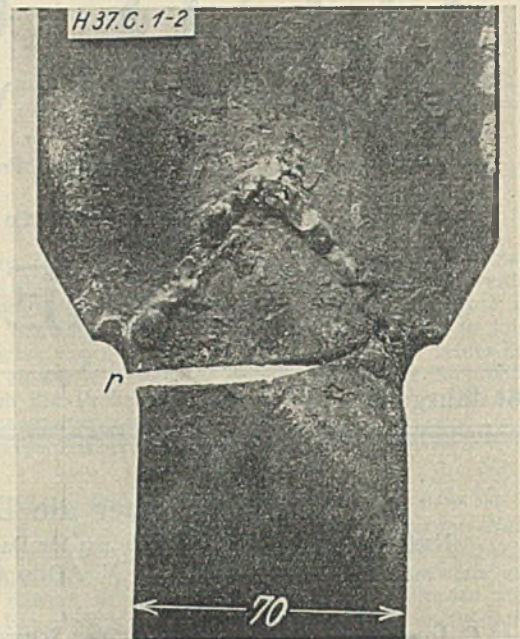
Gasschmelzschweißung nach Abb. 22c; Wurzel nicht nachgeschweißt.
